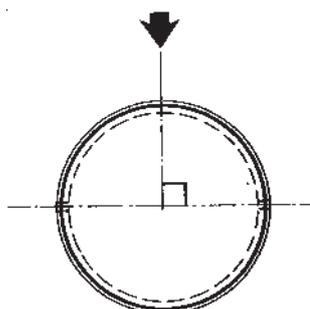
Emplacement de la gorge de segment, turbo KKK
